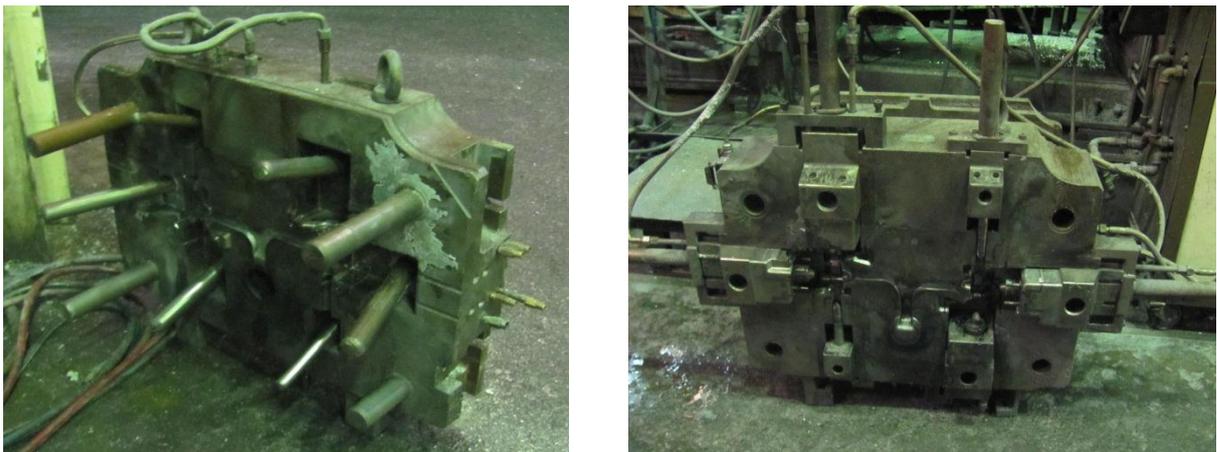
Molde fixo (à esquerda) e Molde móvel com gavetas mecânicas (à direita).
